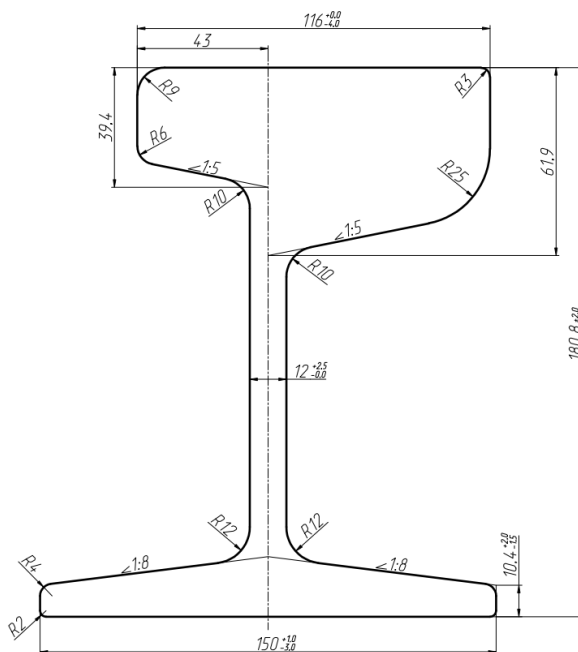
Заготовка трамвайного рельса Т62
